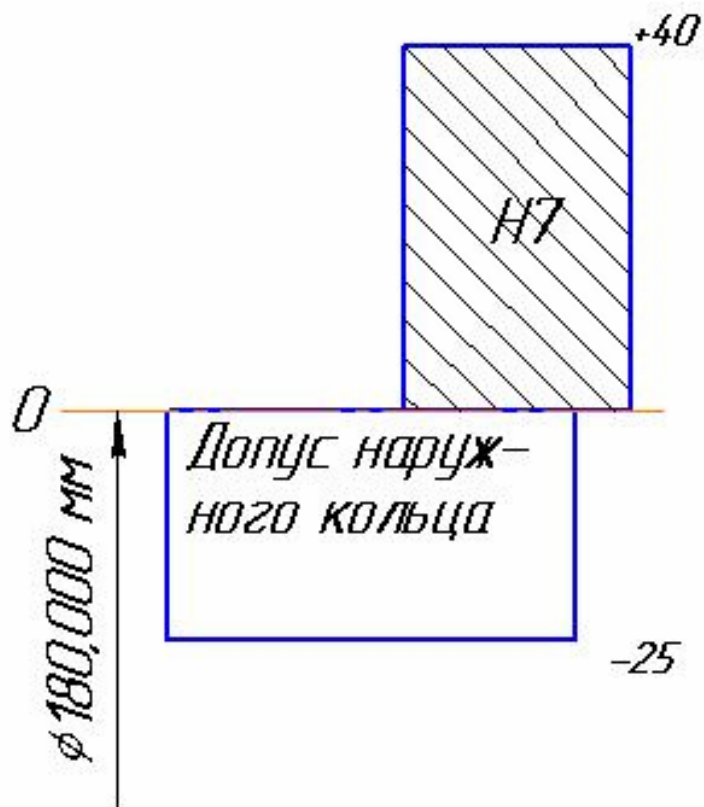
Схема поля допуска посадки наружного кольца с отверстием
